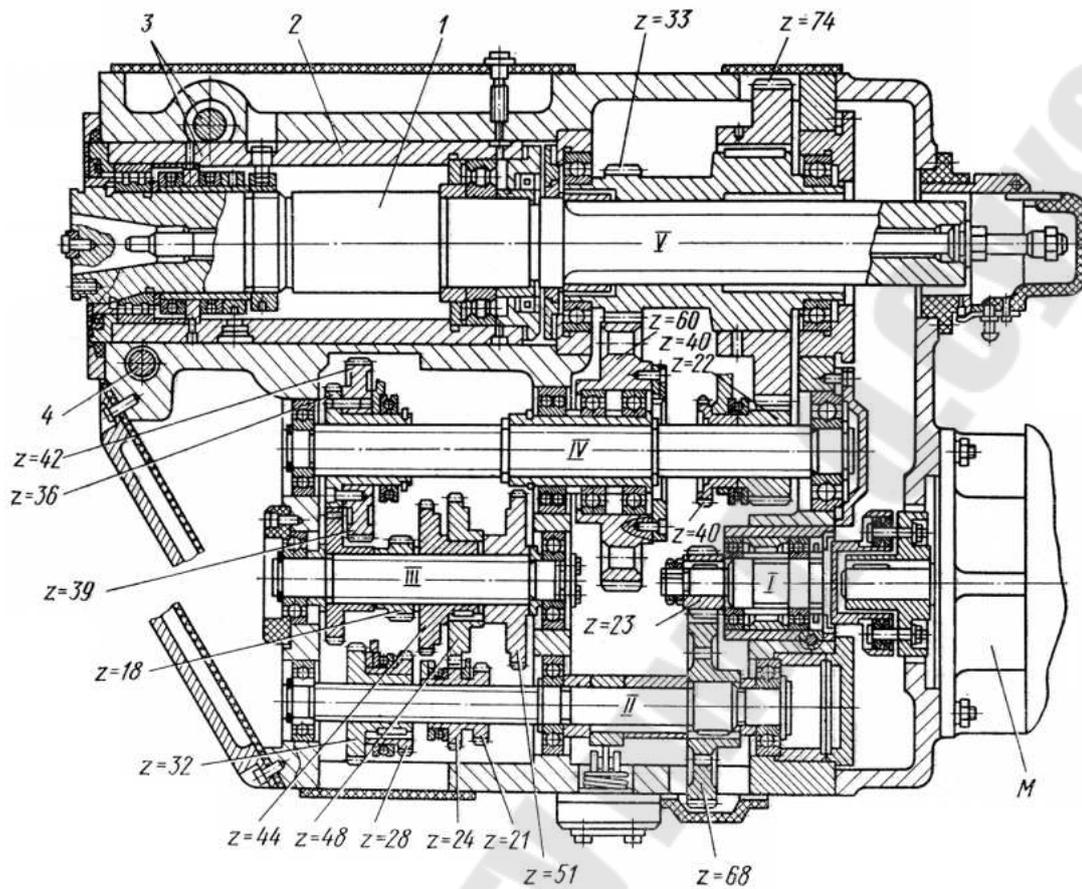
Шпиндельная головка продольно-фрезерного станка:
